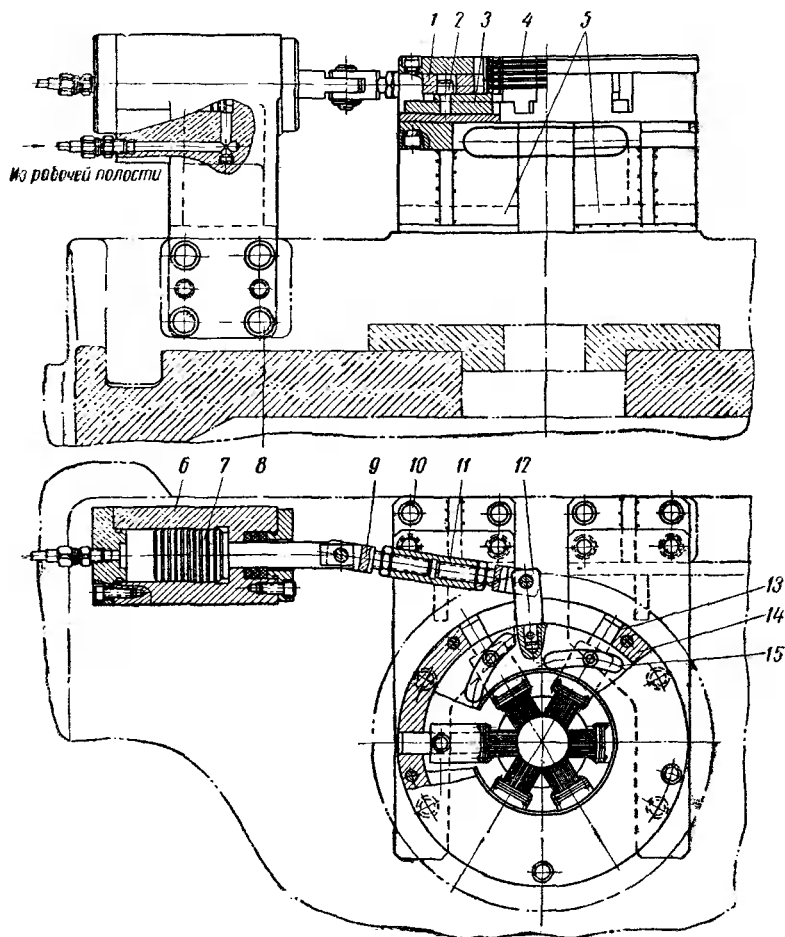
Автоматическое приспособление для очистки протяжек от стружки
